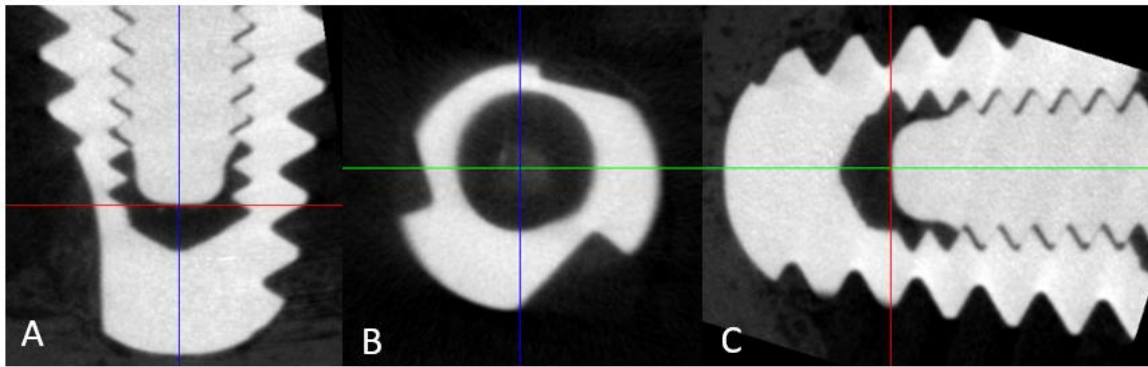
Amostras reconstruídas e padronizadas na posição vertical. A. Plano Transversal; B. Plano Longitudinal; C. Plano Sagital.
